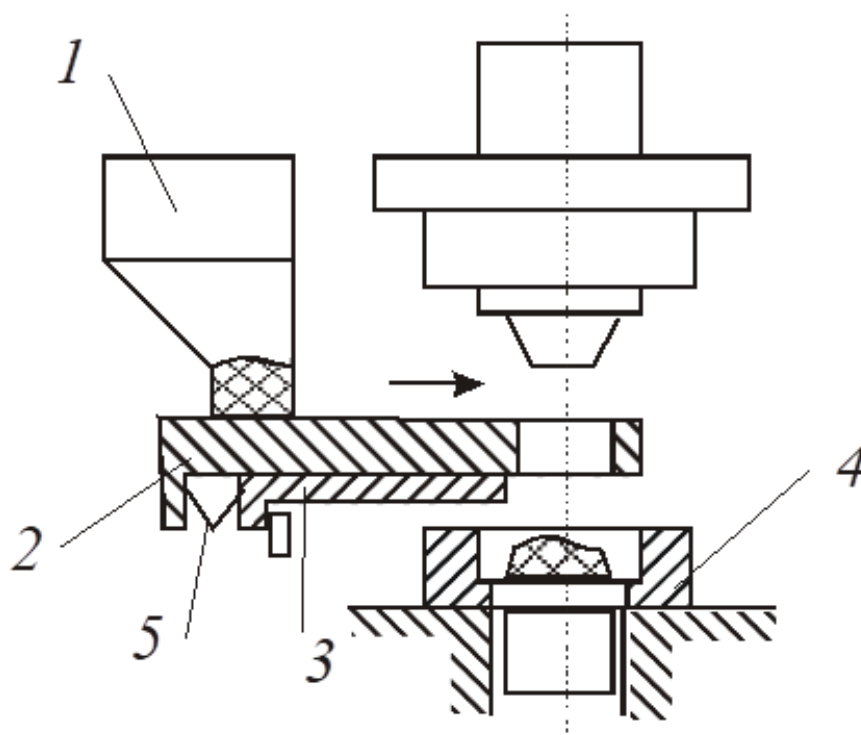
Устройство для загрузки пресс-порошка в пресс-автомат:
